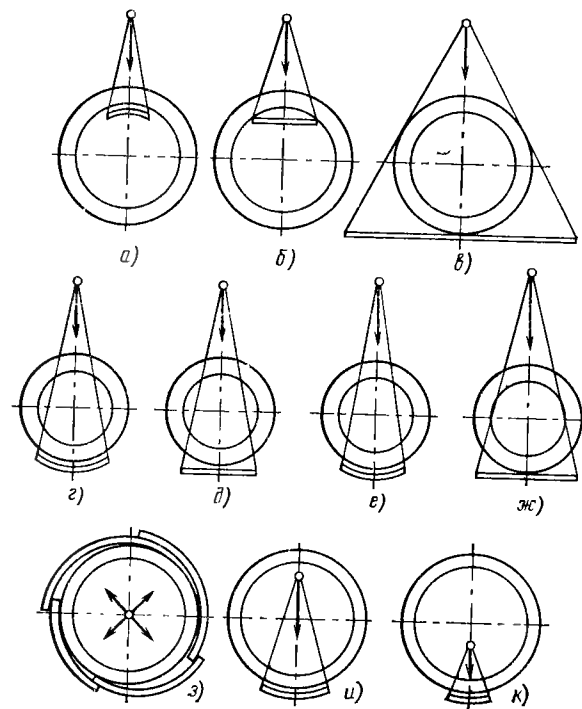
Схемы контроля стыковых сварных соединений цилиндрических и сферических пустотелых изделий.
